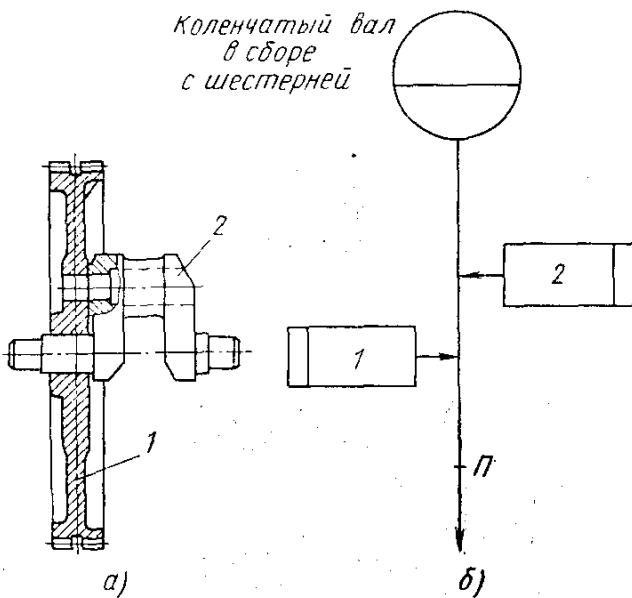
Технологический комплект: а – коленчатый вал; б – схема его сборки; П – запрессовка
